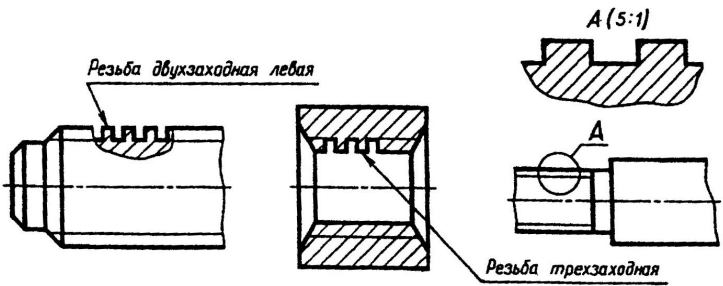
Обозначение резьбы с нестандартным профилем
